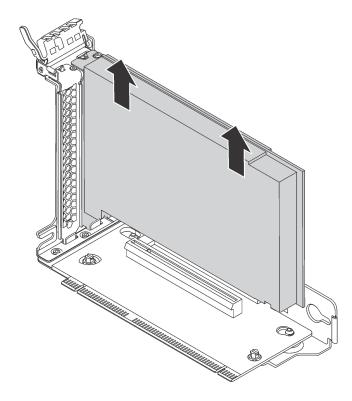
Extracción de un adaptador PCIe del conjunto de expansión
